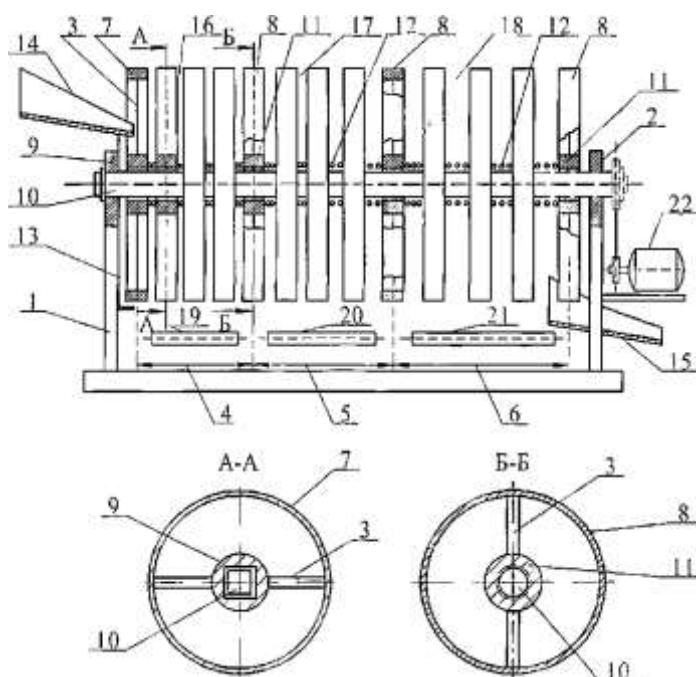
Устройство для очистки и сортировки картофеля:
